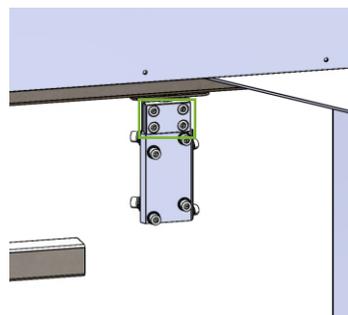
Установленная призма верхнего подшипникового узла
